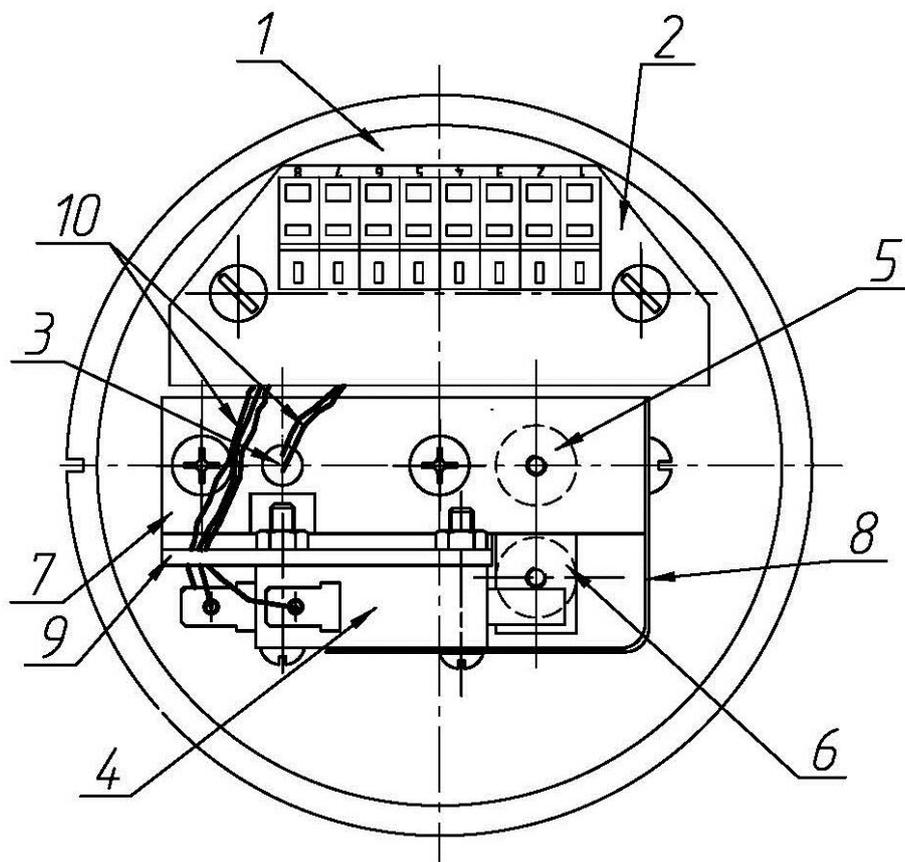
а Габаритный чертёж ручных взрывозащищённых Извещателей ЕхИП535-1В в корпусе из нержавеющей стали, совмещённый с чертежом взрывозащиты. Монтаж кабеля диаметром от 8 до 18 мм.
